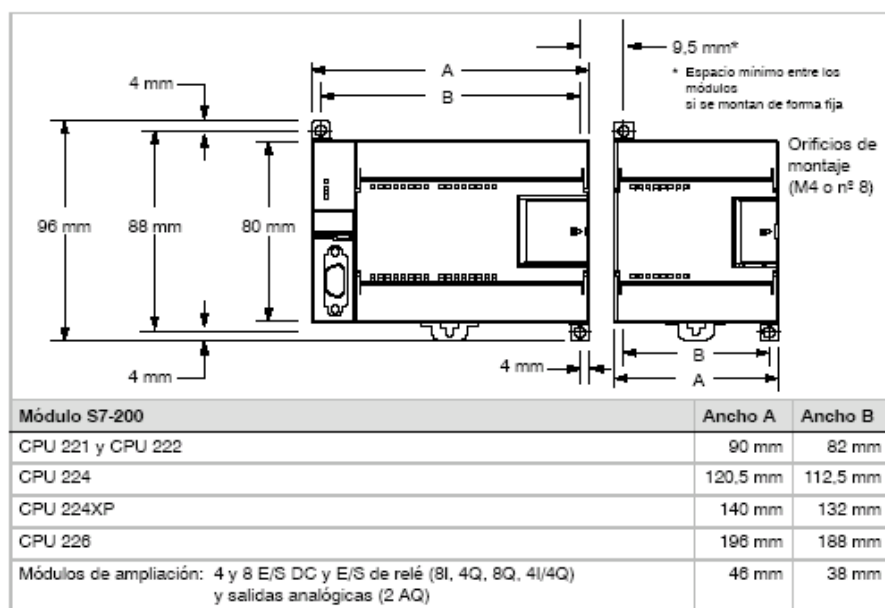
Dimensiones del montaje del PLC y módulos de expansión
